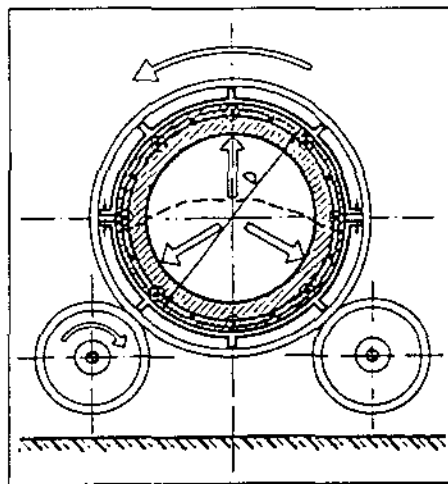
Prinzipskizze einer Rollenbank mit Schleuderform
